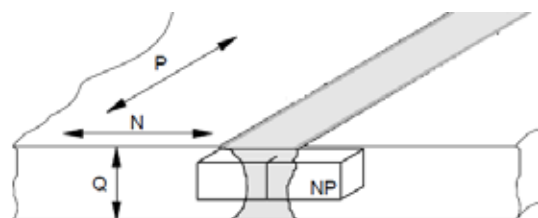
Orientación del plano de crecimiento de la grieta (NP) en las probetas de fractura
